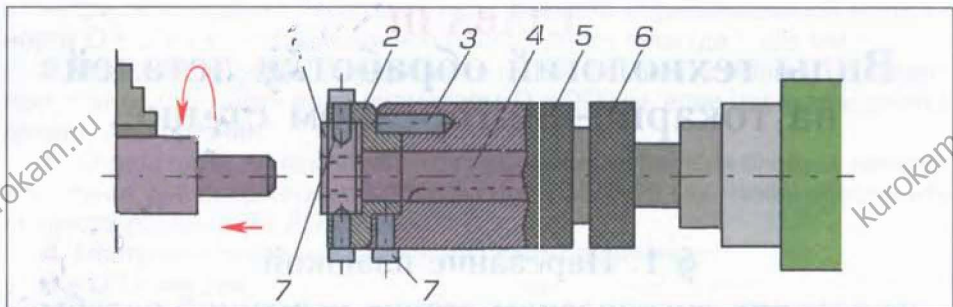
Приспособление для станочного нарезания резьбы малых диаметров
